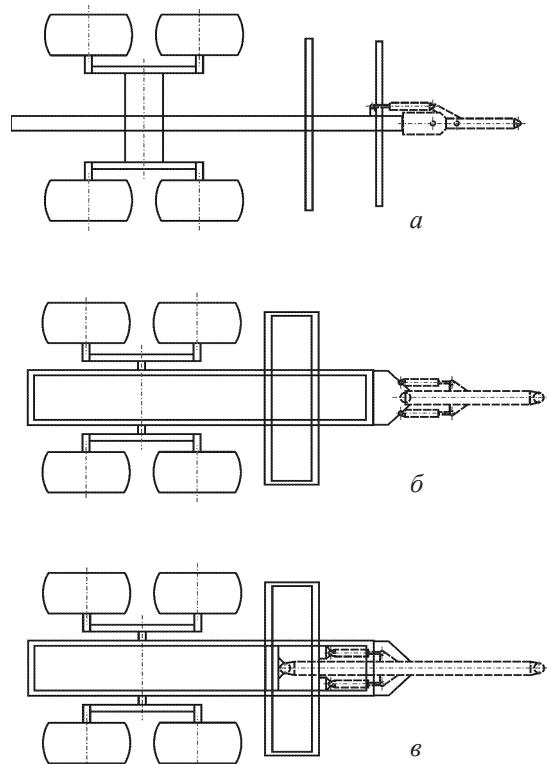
Схемы привода дышла двухзвенного форвардера:
